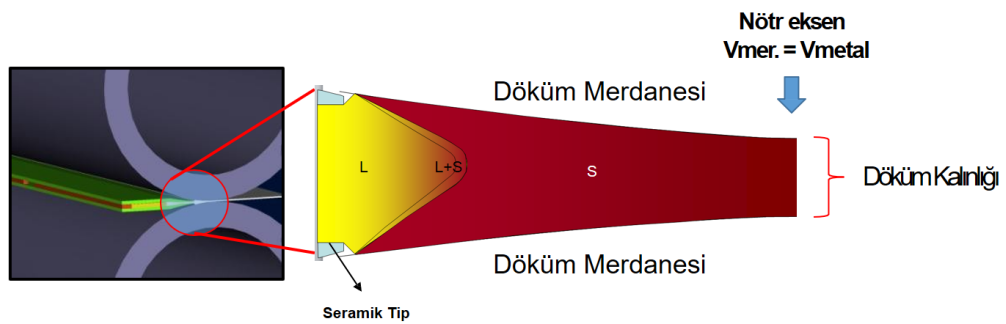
İkiz Merdaneli Sürekli Döküm Hattı Şeması [22].
